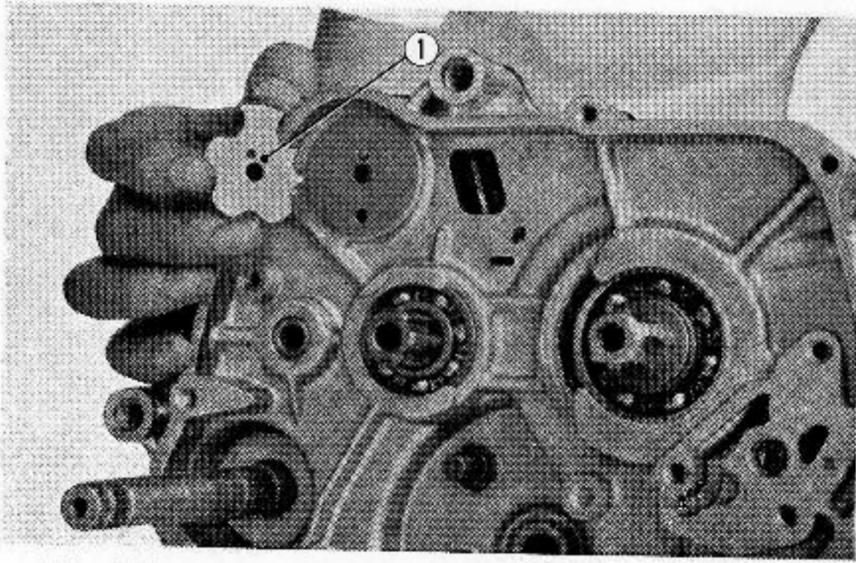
Gabelwellenarretierscheibe ausbauen
